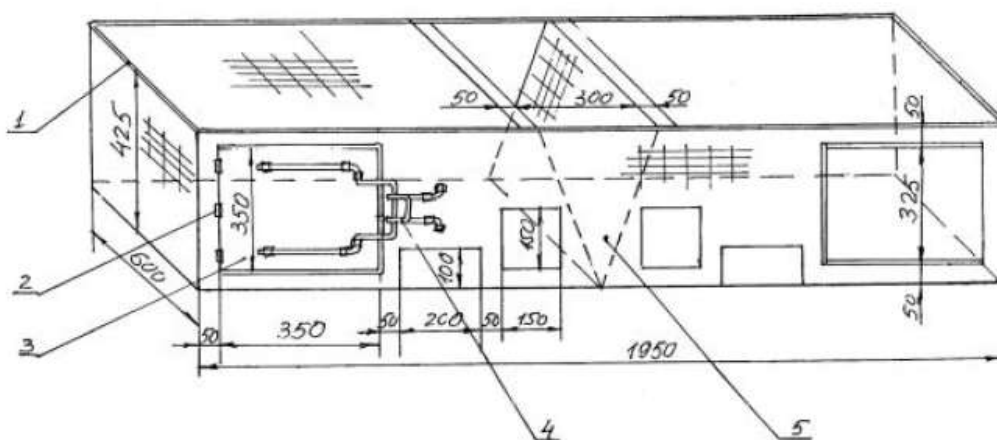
Двухклеточный блок для верхнего яруса: 1 – окантовка блока, проволока ОЦ Ø 3 мм; 2 – скоба большая, сталь ОЦ t=0,8 мм; 3 – дверка клетки; 4 – запор пружинный; 5 – ясли для грубых кормов
